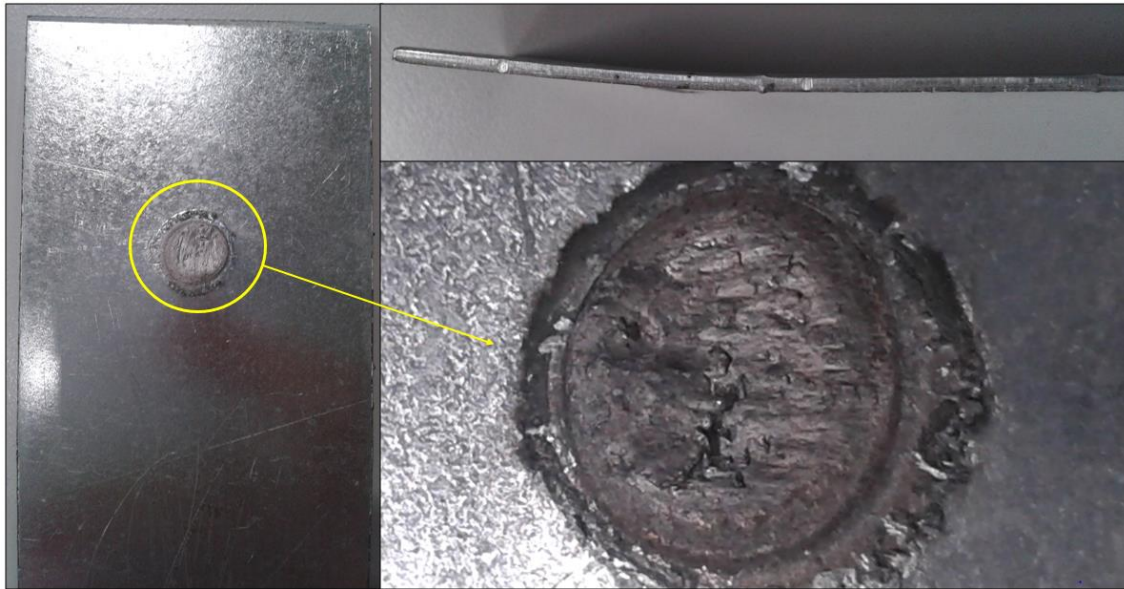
Probetas con daño progresivo en el borde del punto de soldadura. Rotura tipo III.
